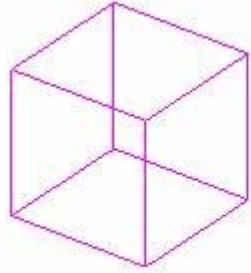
Extrusion (Profil çekme) uygulaması
